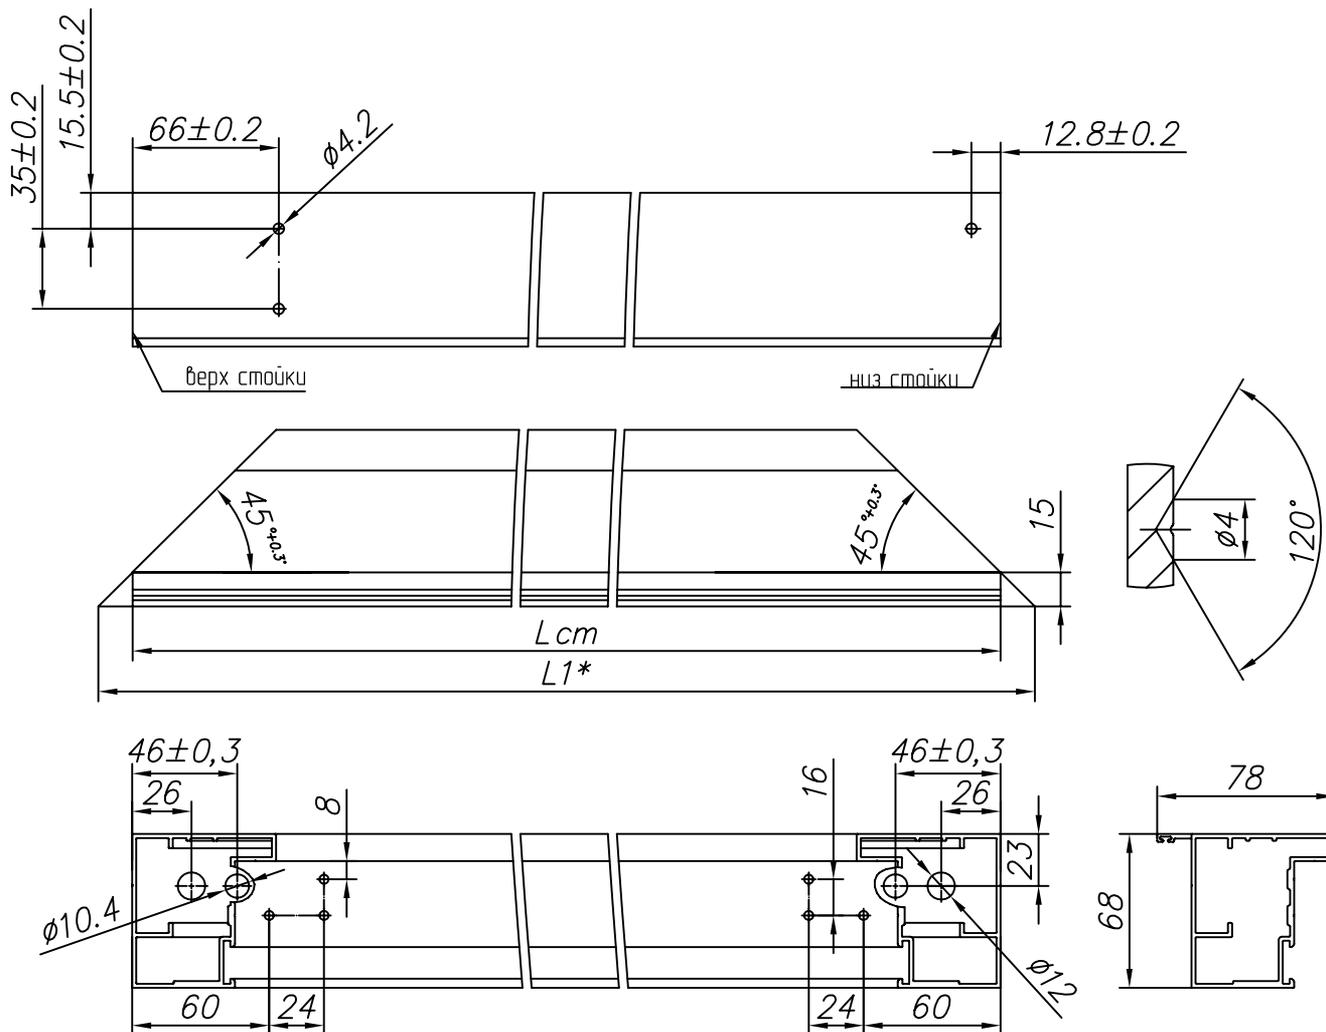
Изготовление стойки из профиля FLGU.400.0108 (стойка левая, открывание калитки наружу)
